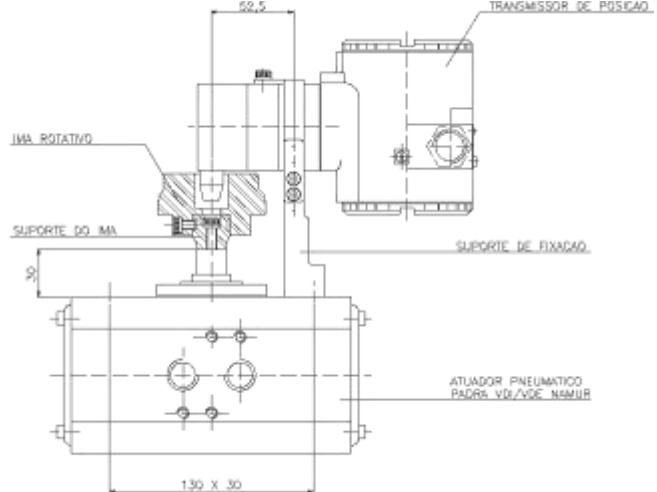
b – Desenho Dimensional do Sensor Remoto
